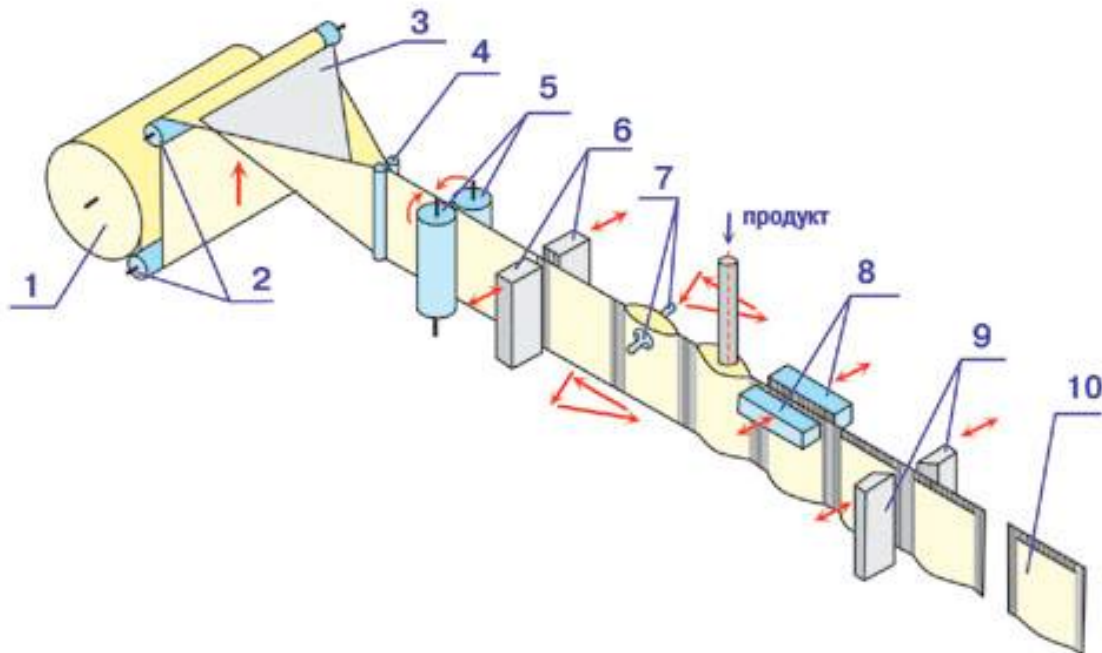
Горизонтальне лінійне компонування машини: 1 – рулон плівки; 2 – натяжні валки; 3 – направляюча; 4 – формуючі валки; 5 – ролики протяжки; 6 – пристрій зварювання бокових швів; 7 – вакуумні захвати; 8 – пристрій зварювання верхнього шва; 9 – механізм відрізання; 10 – готовий пакет
